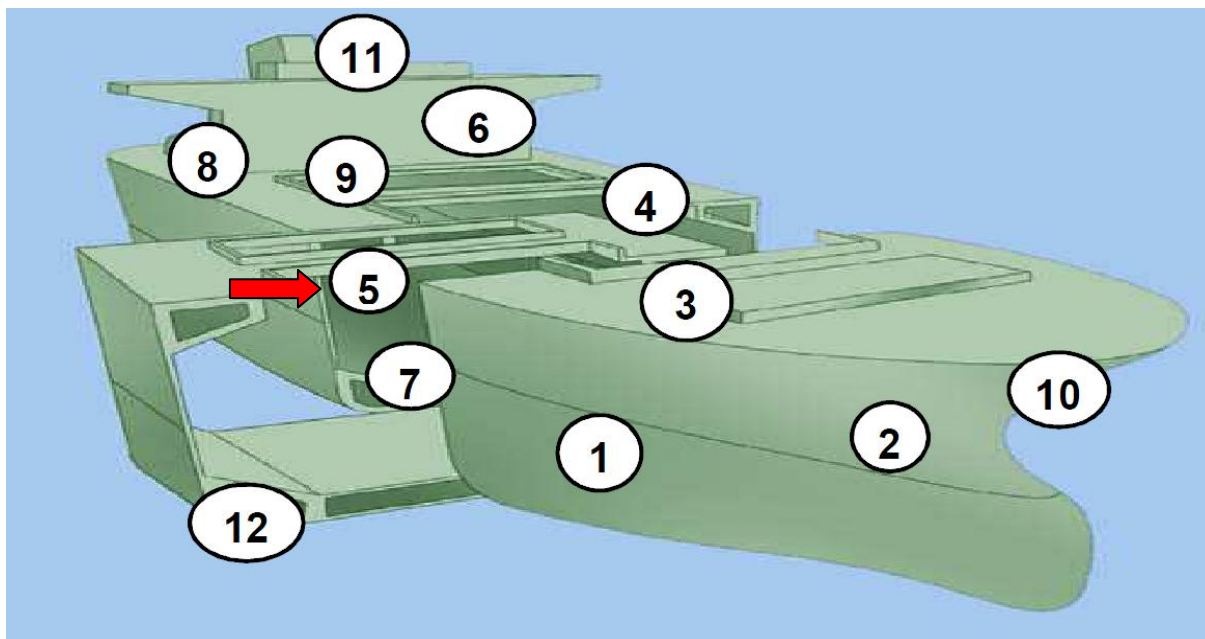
Esquema de pintado de los espacios debajo de la cubierta principal
